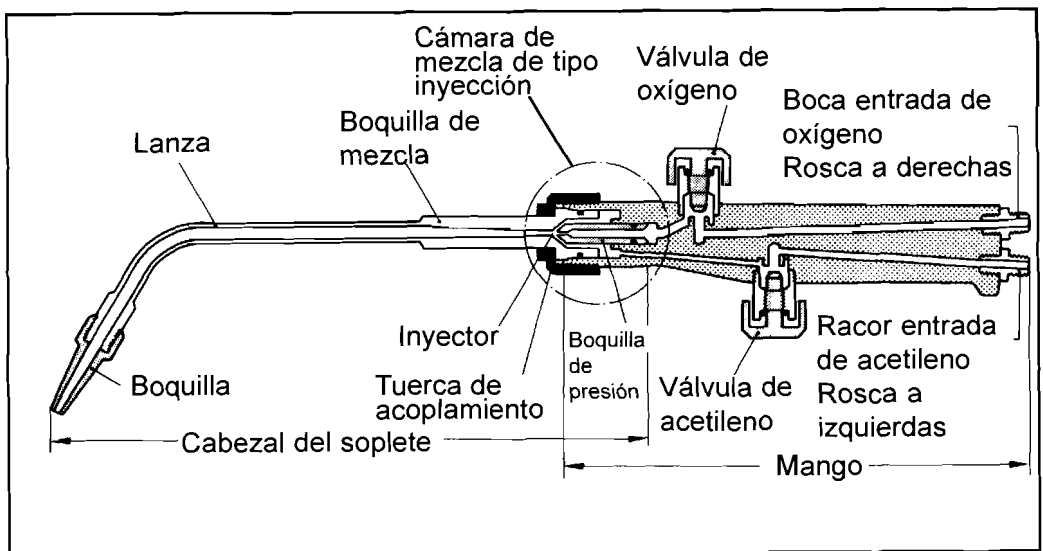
SOPLETE DE INYECCIÓN PARA SOLDEO OXIACETILÉNICO
